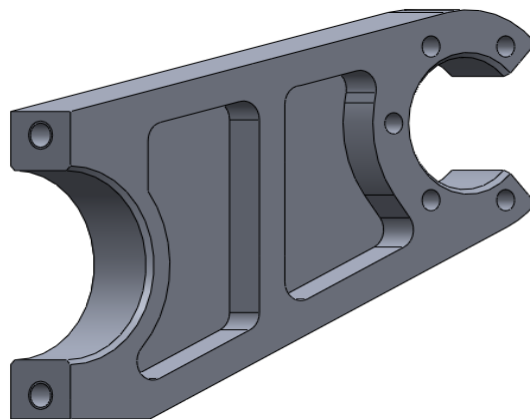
| Suporte frontal do gerador elétrico.
